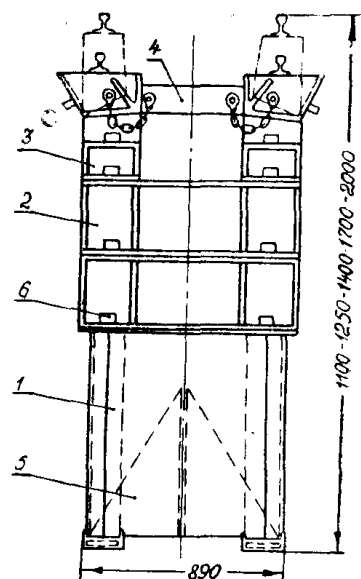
Неразборный передвижной костер ПМК-2 конструкции Гипроуглемаша. 1—стул костра; 2—рамные надставки, 3—подставка; 4—замковая балка; 5—лобовина; 6—бобышки
